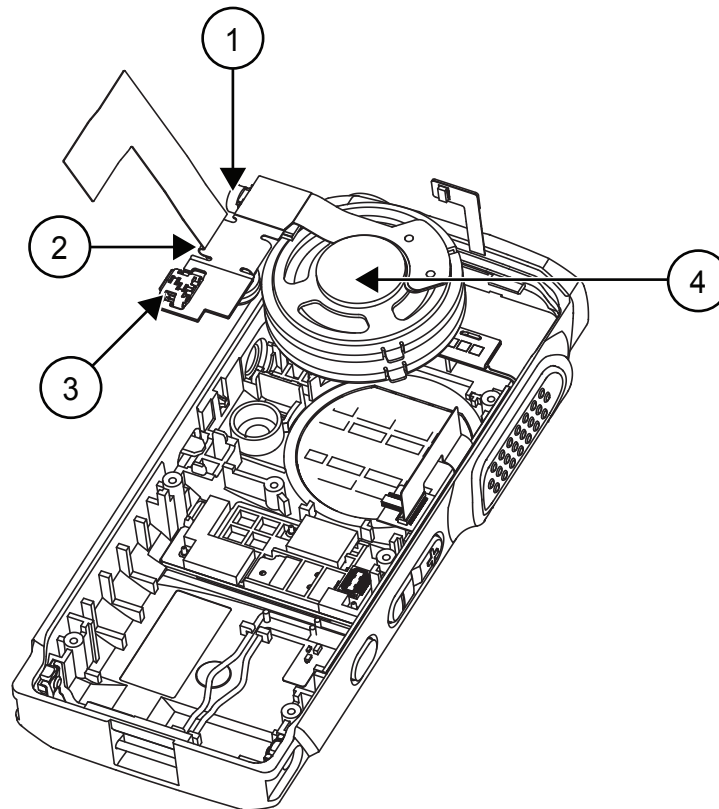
Demontaż śrub wewnętrznej ramki
